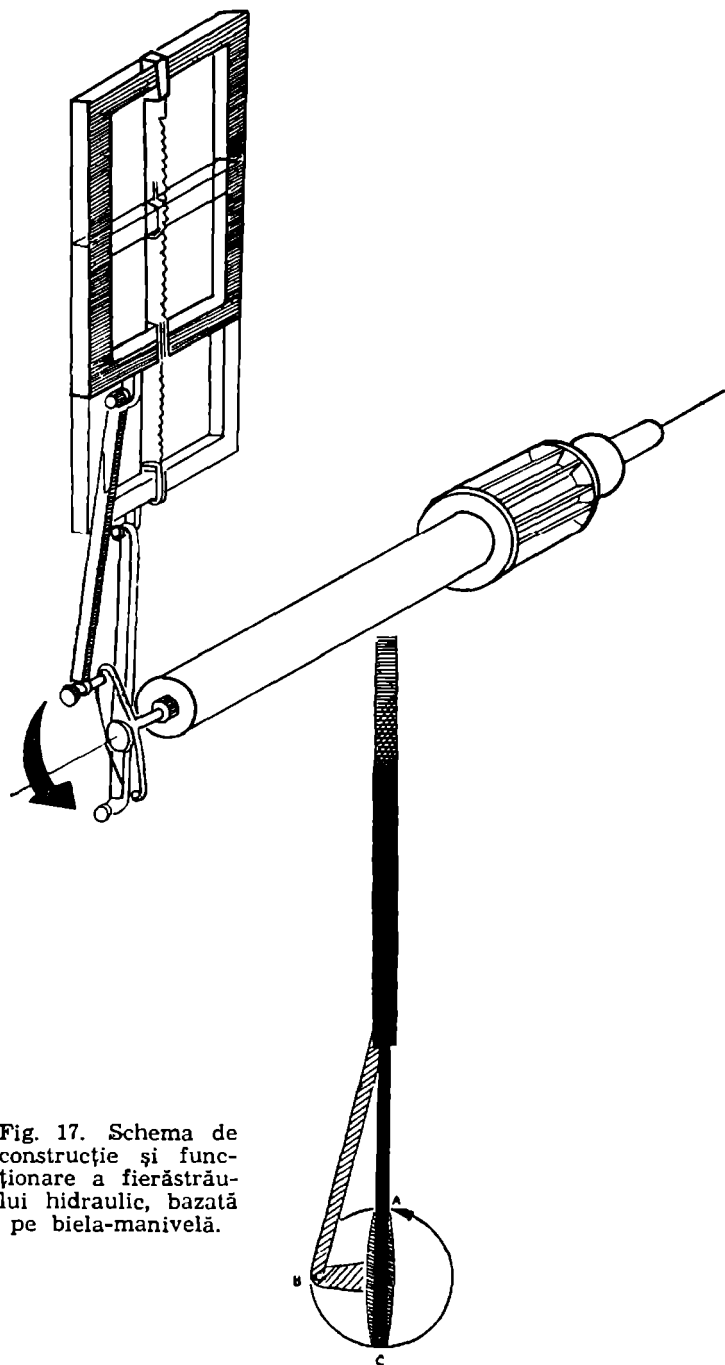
Schema de construcție și funcționare a fierăstrăului hidraulic, bazată pe biela-manivelă.
